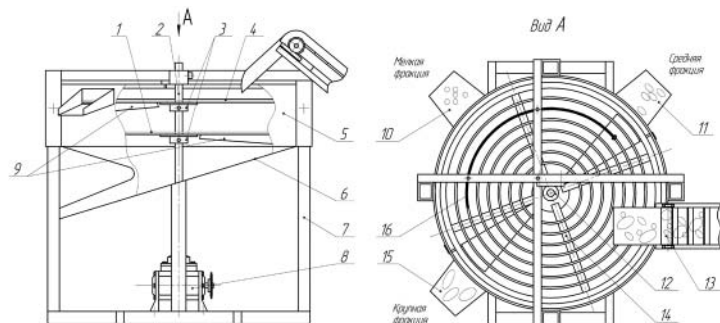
Общий вид плоской круглорешетной сортировки: 1 - решето №2; 2 - вал; 3 - ступица; 4 - решето №1; 5 - обод кожура; 6 - приемник; 7 - рама; 8 - редуктор; 9 - подъемная планка; 10 - выгрузной лоток мелкой фракции; 11 - выгрузной лоток средней фракции; 12 - подшипник; 13 - питающий транспортер; 14 - спица; 15 - выгрузной лоток крупной фракции; 16 - сектор-обод.
